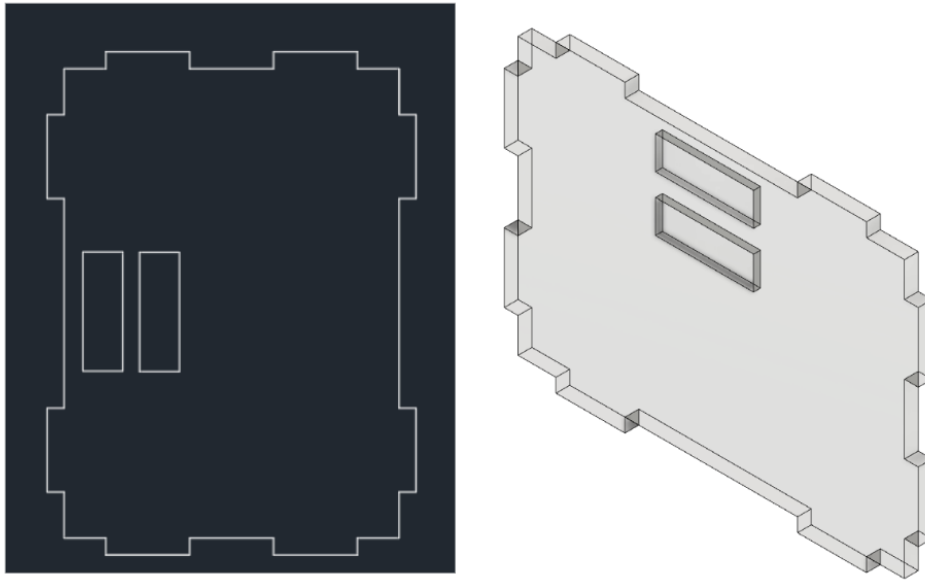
Diseño de la pared frontal de la estructura en el CAD Fusión 360 en vista isométrica
